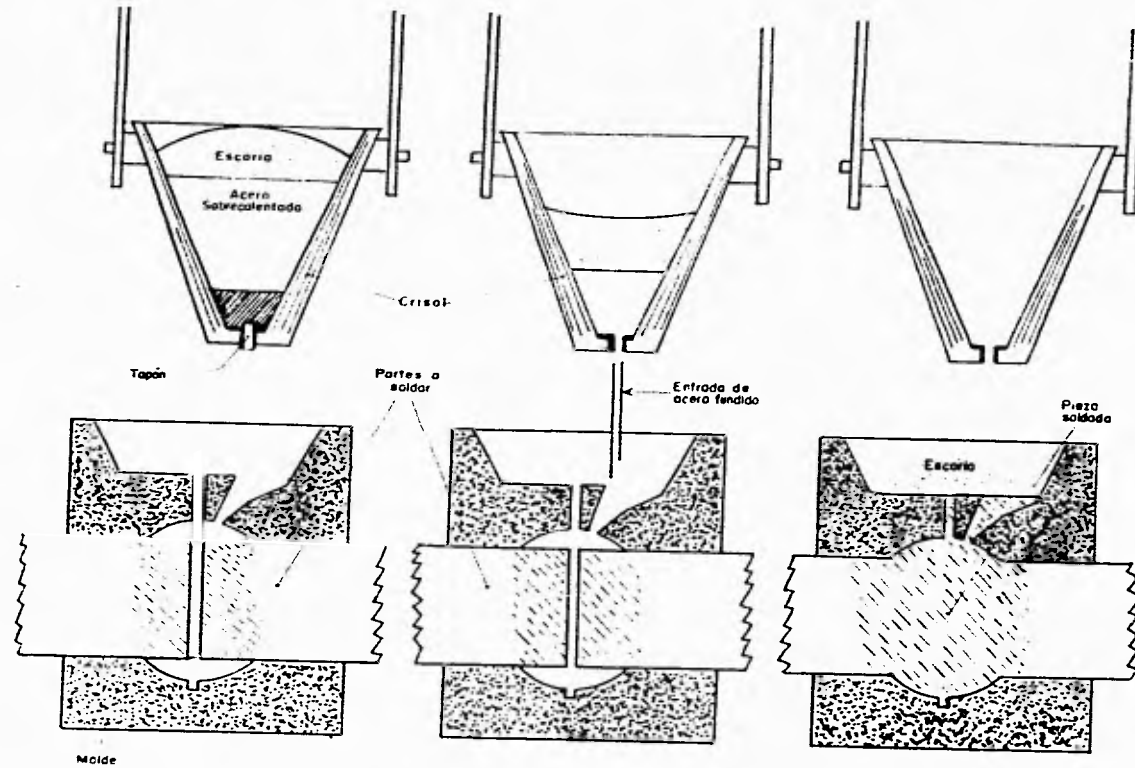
Soldadura por termita (TW)
